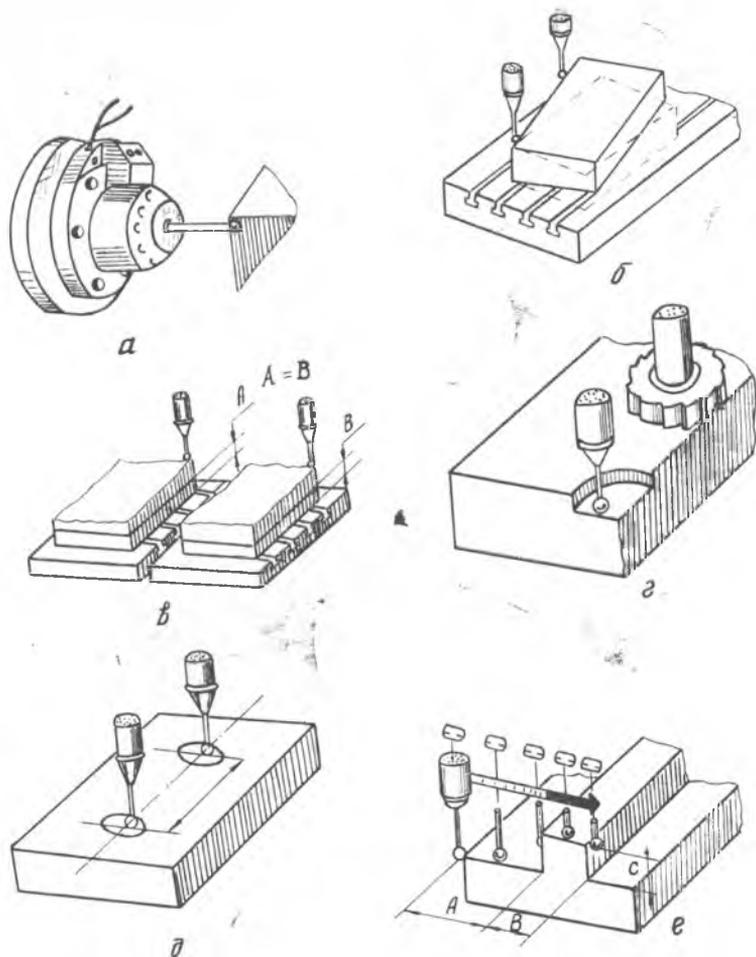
Схемы применения шупов на станке с ЧПУ типа ОЦ для измерения: а — установки нулевой точки; б — погрешности установки заготовки на столе; в — снимаемого припуска; г — припуска на чистовой переход; д — межосевого расстояния; е — обработанной детали
